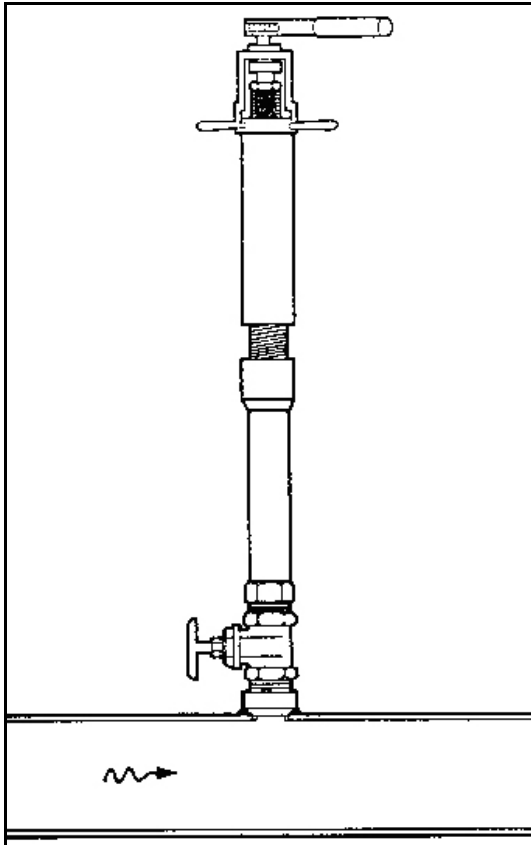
Bohrmaschine mit Adapter auf Absperrventil
